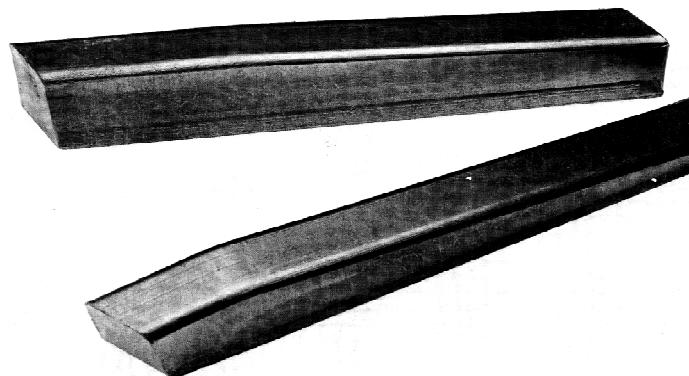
Внешний вид центральной и одной боковой частей вставки
